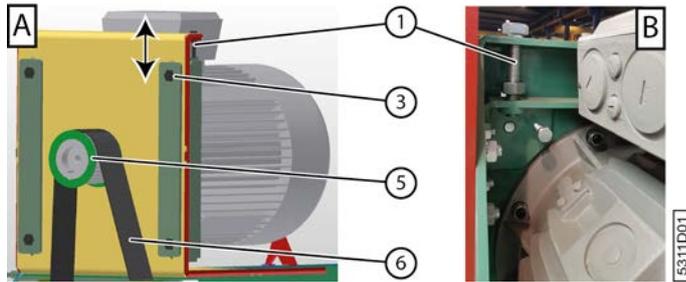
Vue avant [A] et vue arrière détaillée [B] du moteur électrique
